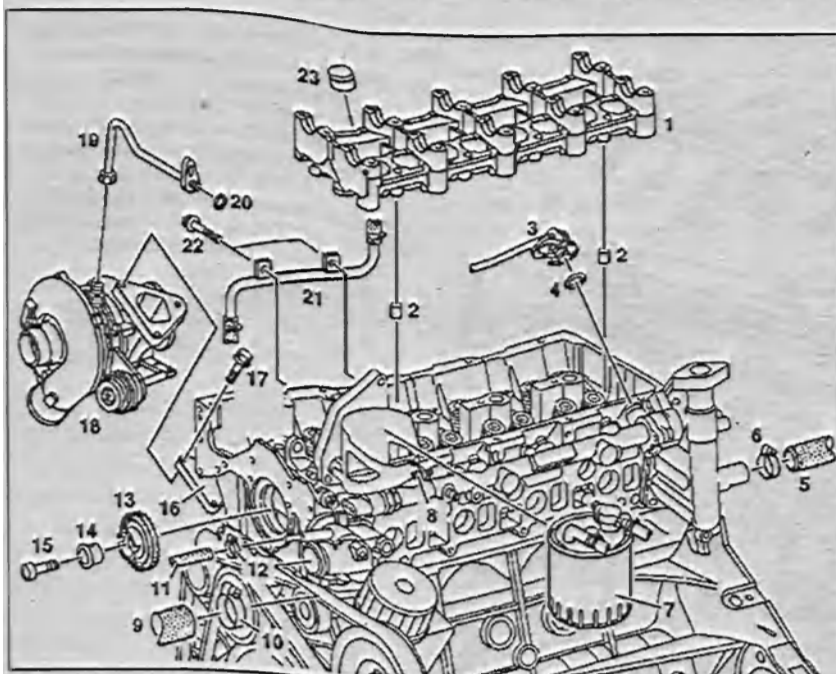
а. Снятие и установка головки блока цилиндров (показано на двигателях 611):
